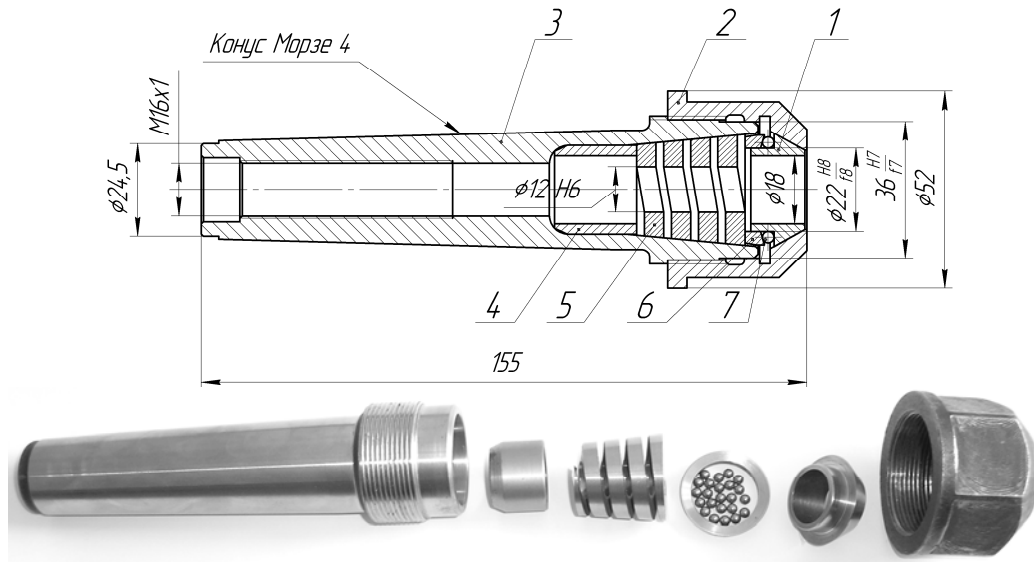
Досліджуваний інструментальний затискний патрон: робоче креслення(зверху) та дослідний зразок(знизу)
